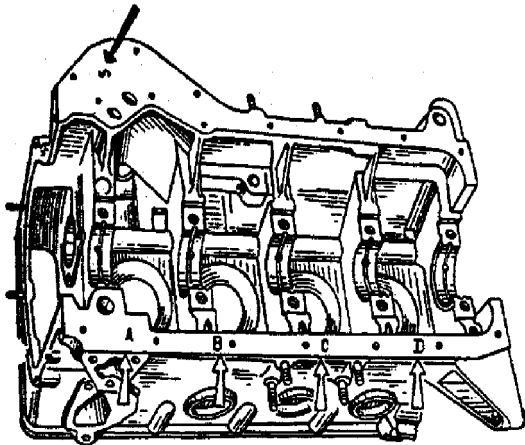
Marcações do bloco de cilindros: grupo dimensional - flexas brancas; número convencional do bloco - flexa preta.
